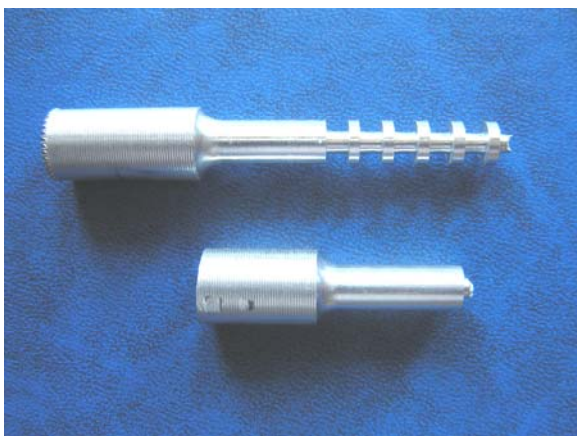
Фотография разрушенного в ходе испытаний на растяжение образца из алюминиевого сплава 1201-T1 с прямоугольными выточками
